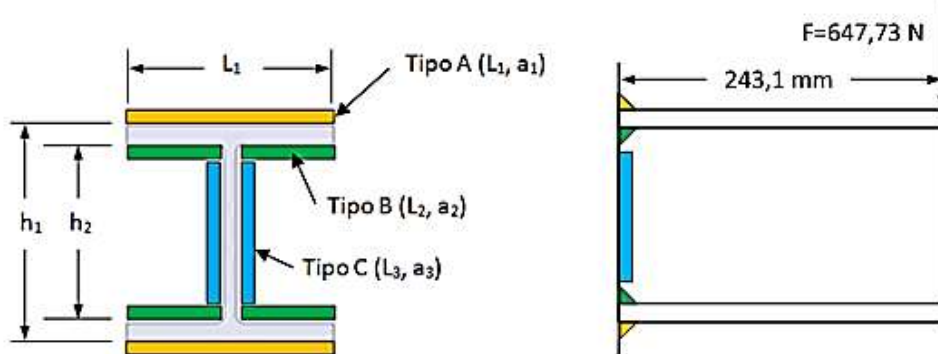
Soldadura en el perfil de la viga HEB 100
